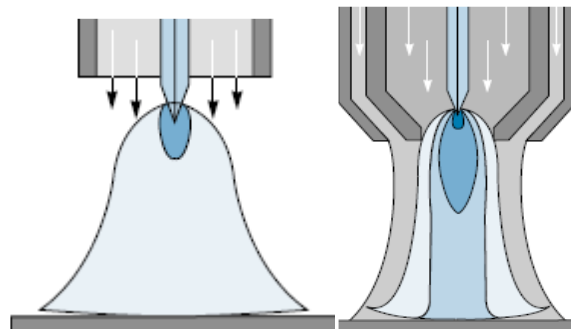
Procédé de soudage TIG (GTAW) et plasma (PTAW) [1].
